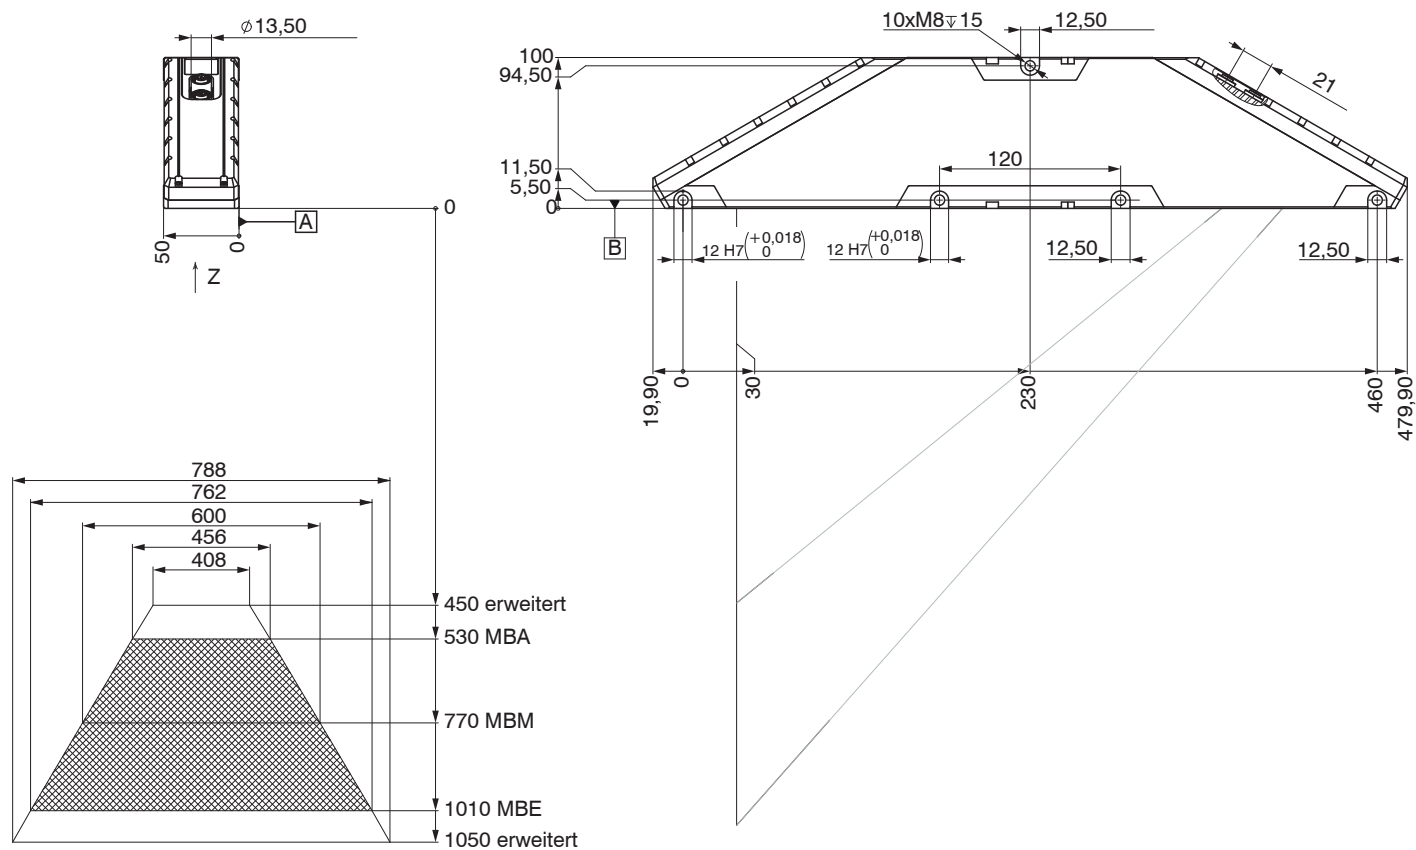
Maßzeichnung Sensor scanCONTROL 30xx-600
